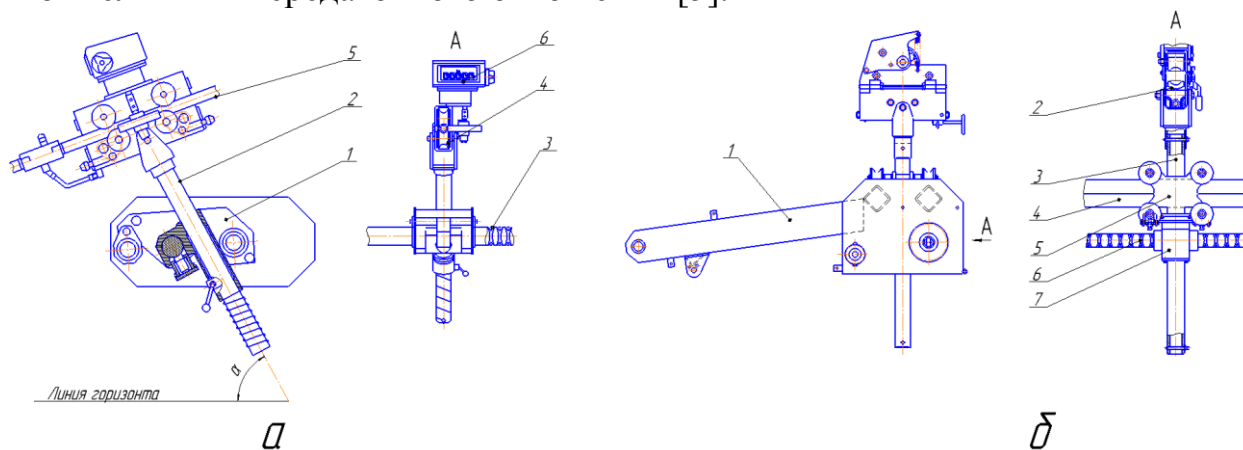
Общий вид укладчика безмуфтовой длинномерной трубы
